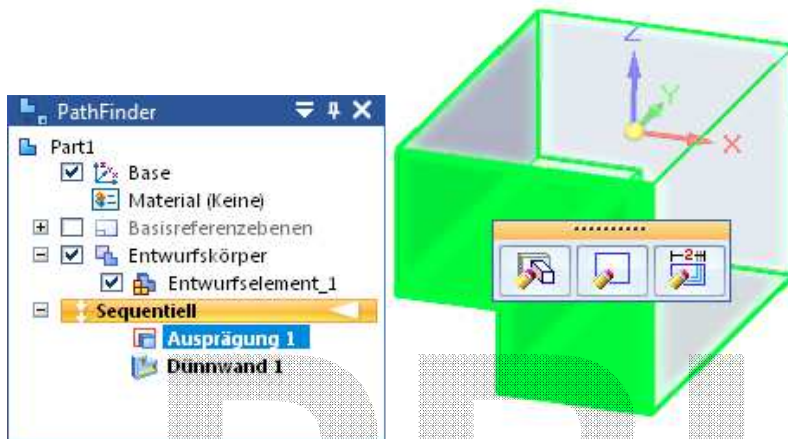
QuickBar zur Bearbeitung gewählter Formelemente
